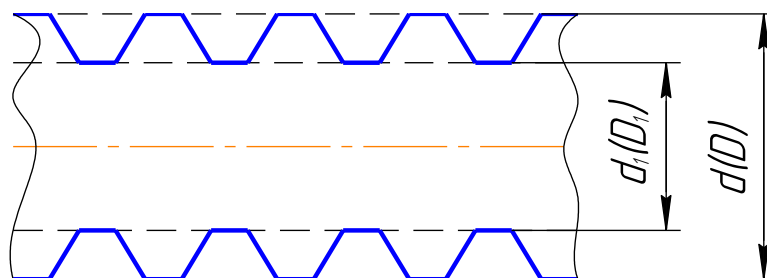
Схема измерения наружного и внутреннего диаметров резьбы
